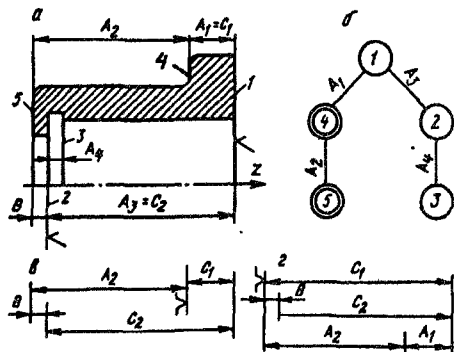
Пример выбора базы для первой операции изготовления детали типа втулки
